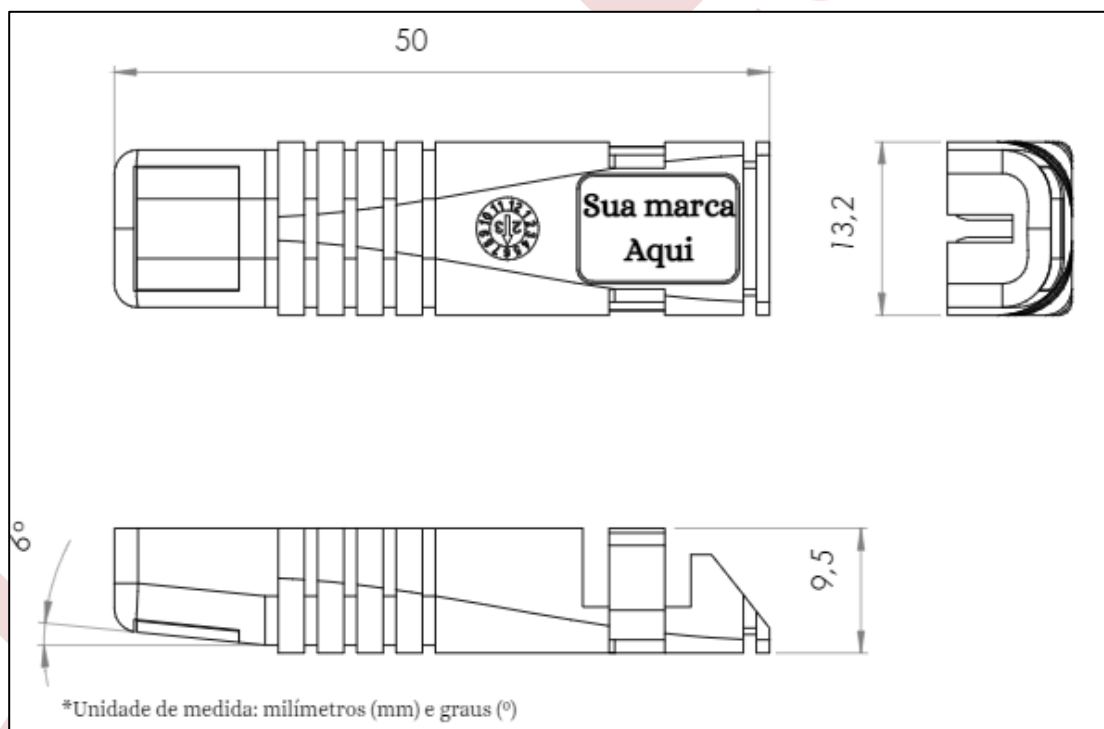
DIMENSIONAL PROTETOR PARA INSTALAÇÃO ATIVA
